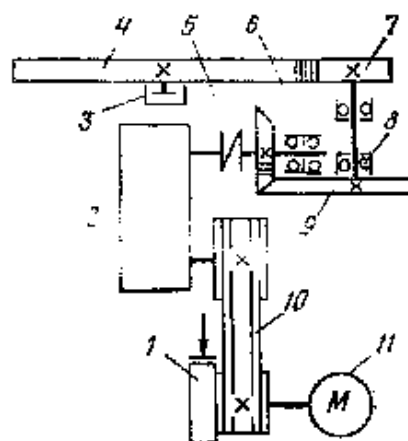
Кинематическая схема станка СМЖ-179А:
